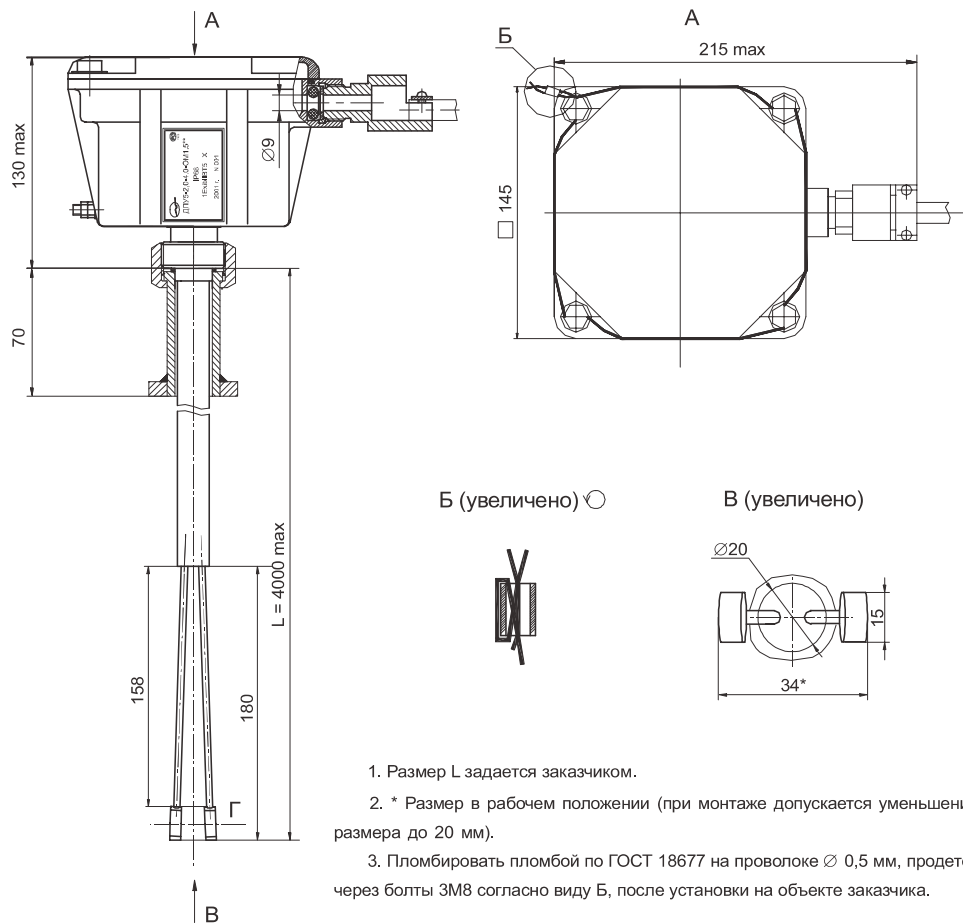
Габаритные размеры датчика ДПУ5
